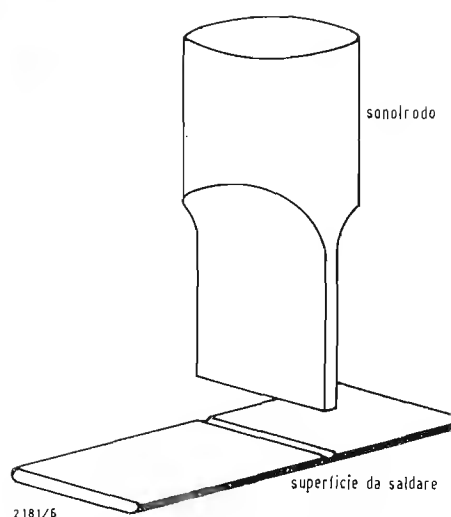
Forma del sonotrodo per la saldatura di materiale tubolare.
